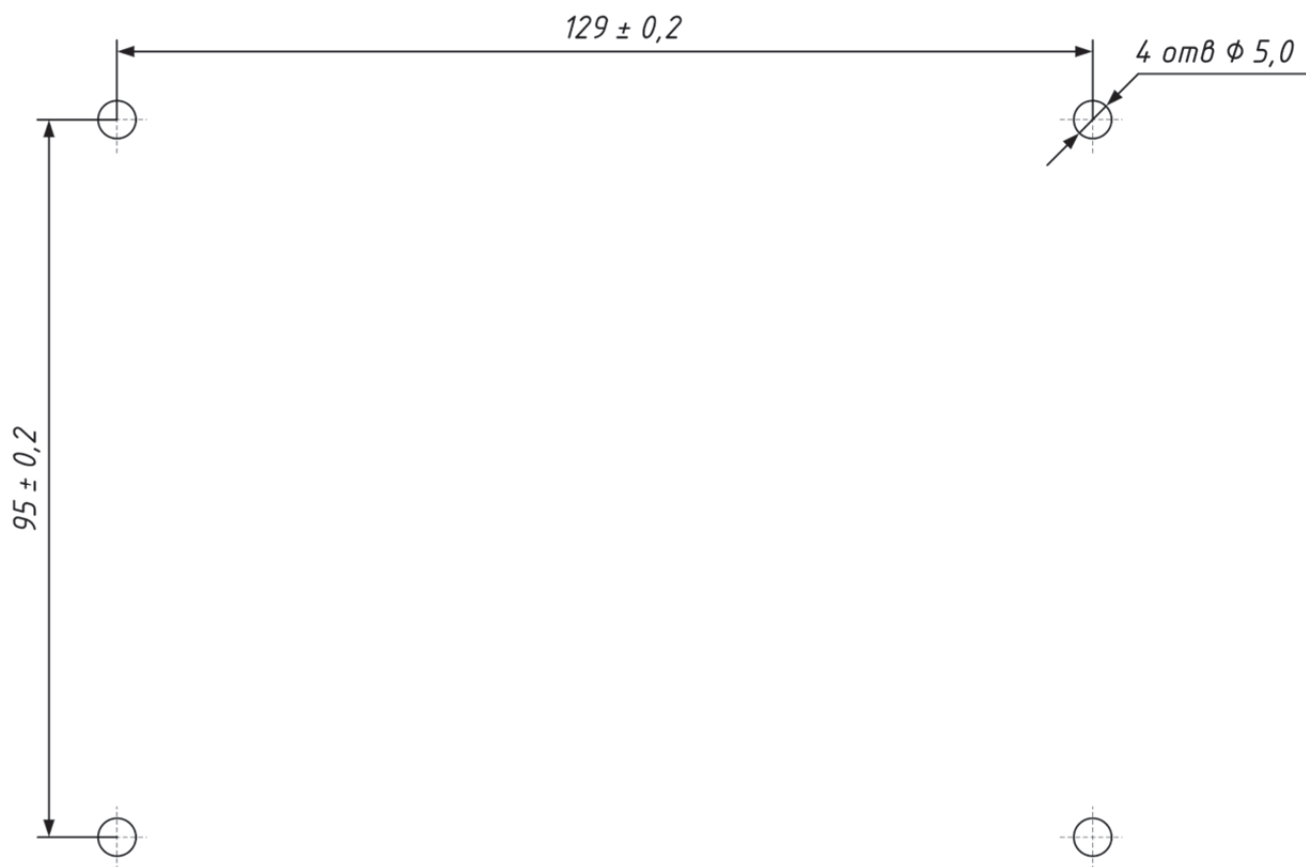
Чертеж сверловки для установки ПРОЭЛ-МИНИ-00
